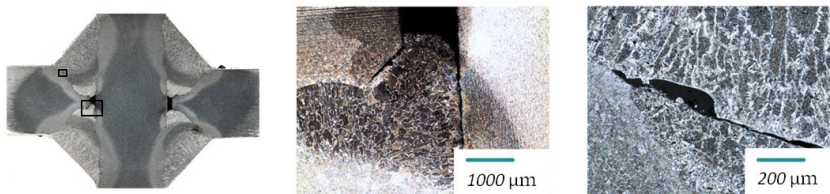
Makro- und Mikroschliffe eines Kreuzstoßes mit inneren Schweißnahtimperfectionen [1]
